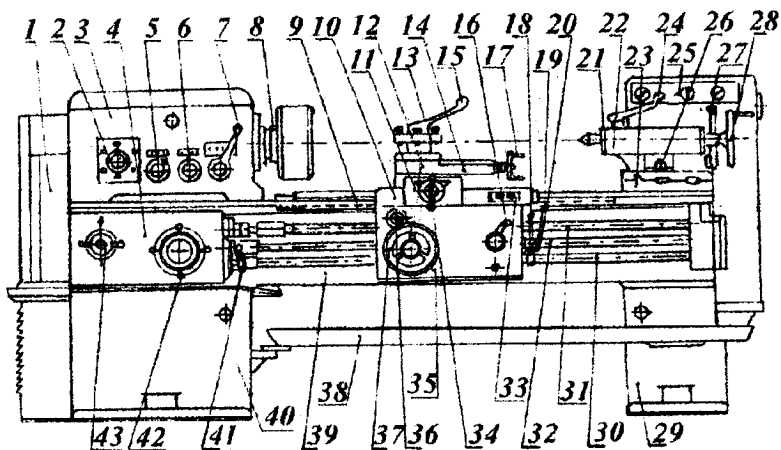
Загальний вид токарно-гвинторізного верстата 1K62
